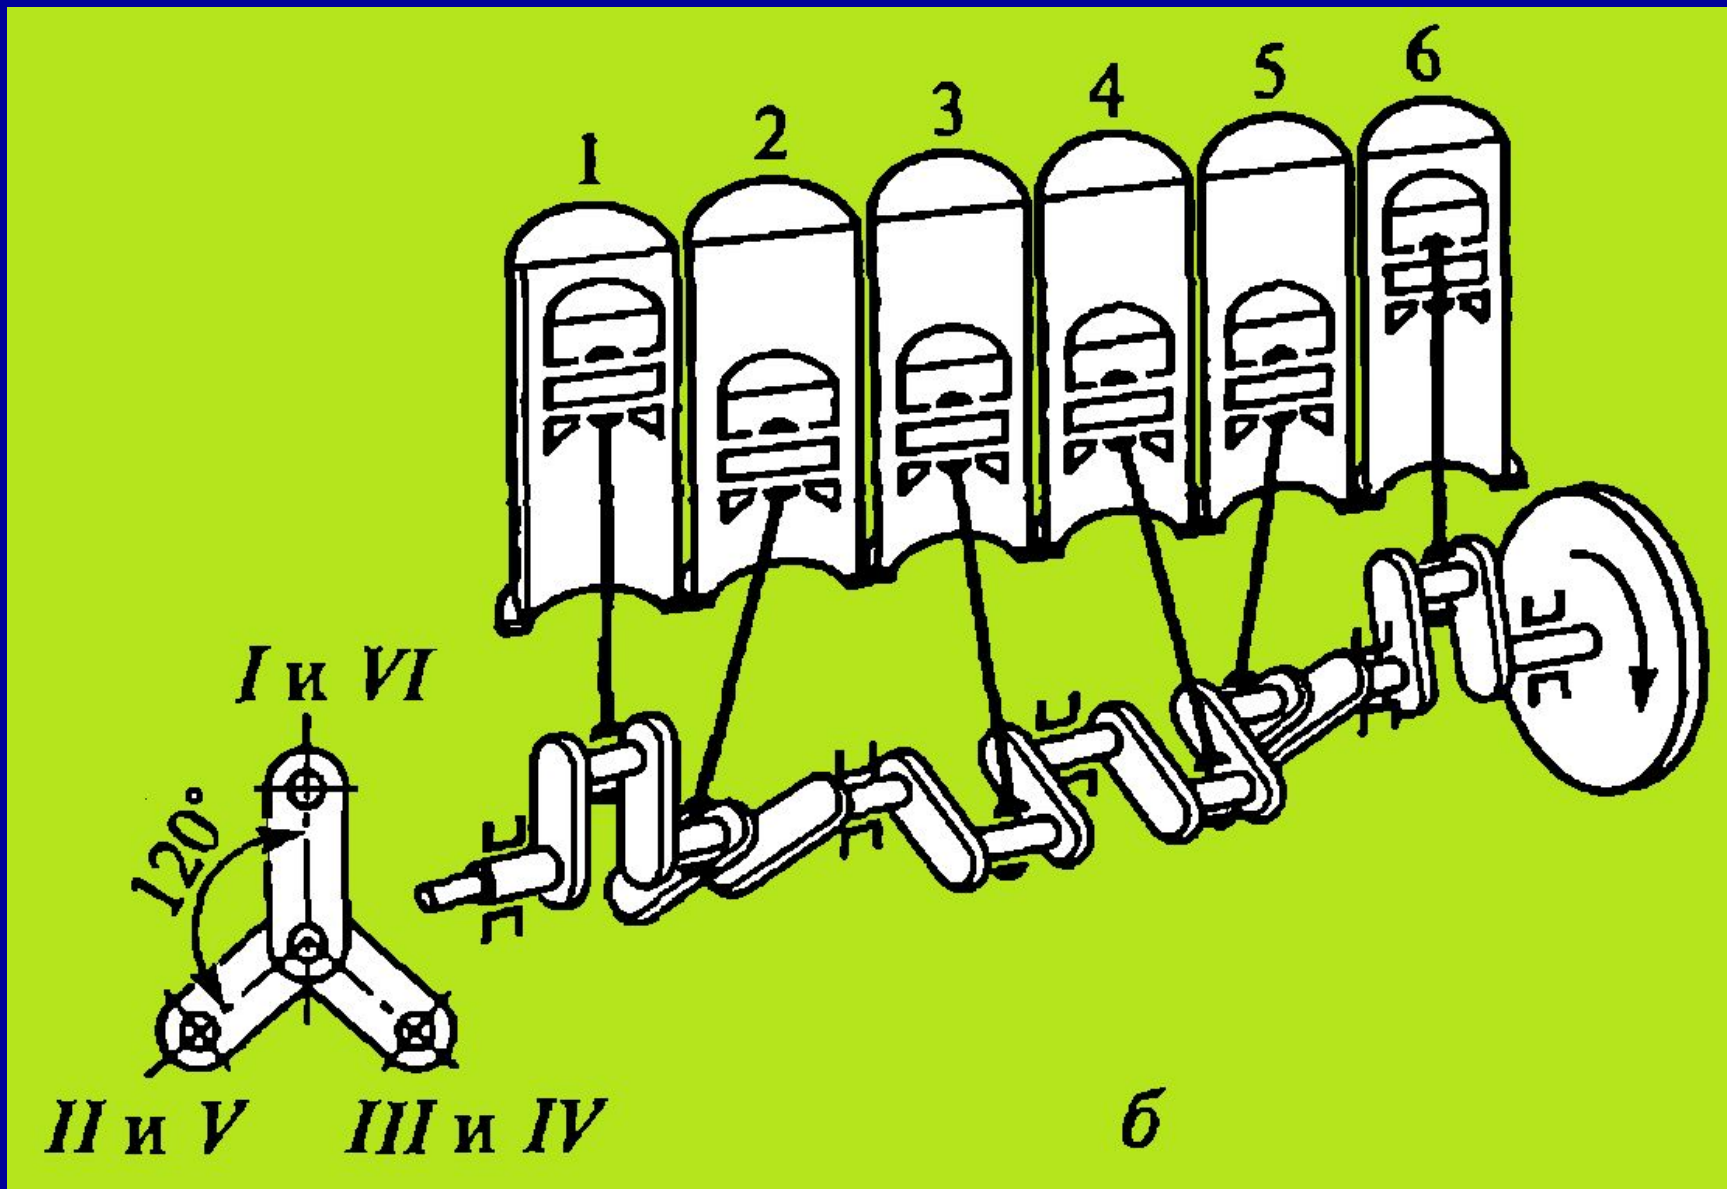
б. Схема кривошипно-шатунного механизма четырехтактного шестицилиндрового рядного двигателя.
